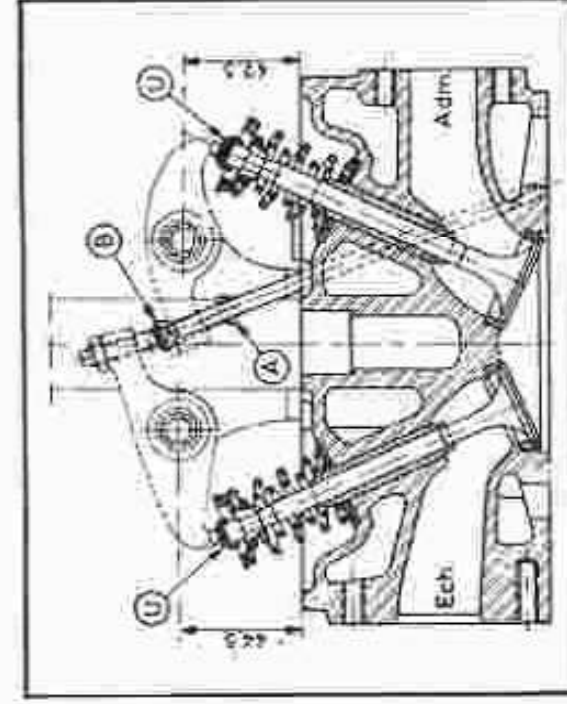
Vue en coupe du premier montage des rampes de culbuteurs.
